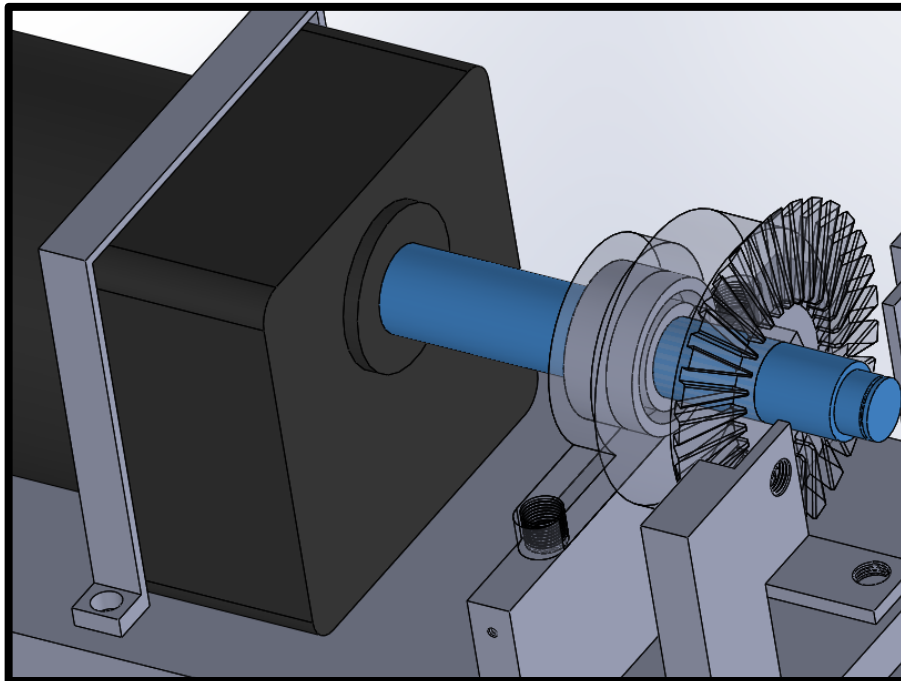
Detalle del eje de unión entre el motor y el piñón. Fuente: Propia.
